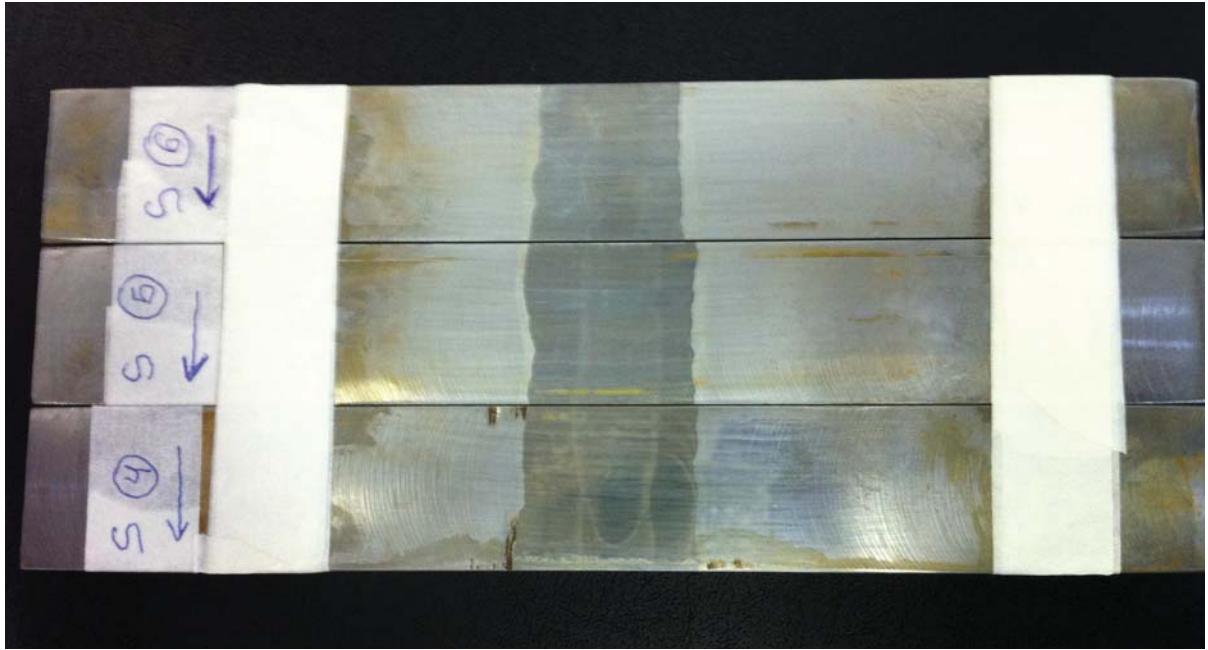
Corpos de prova SE (B) (solda) após o ataque químico.
